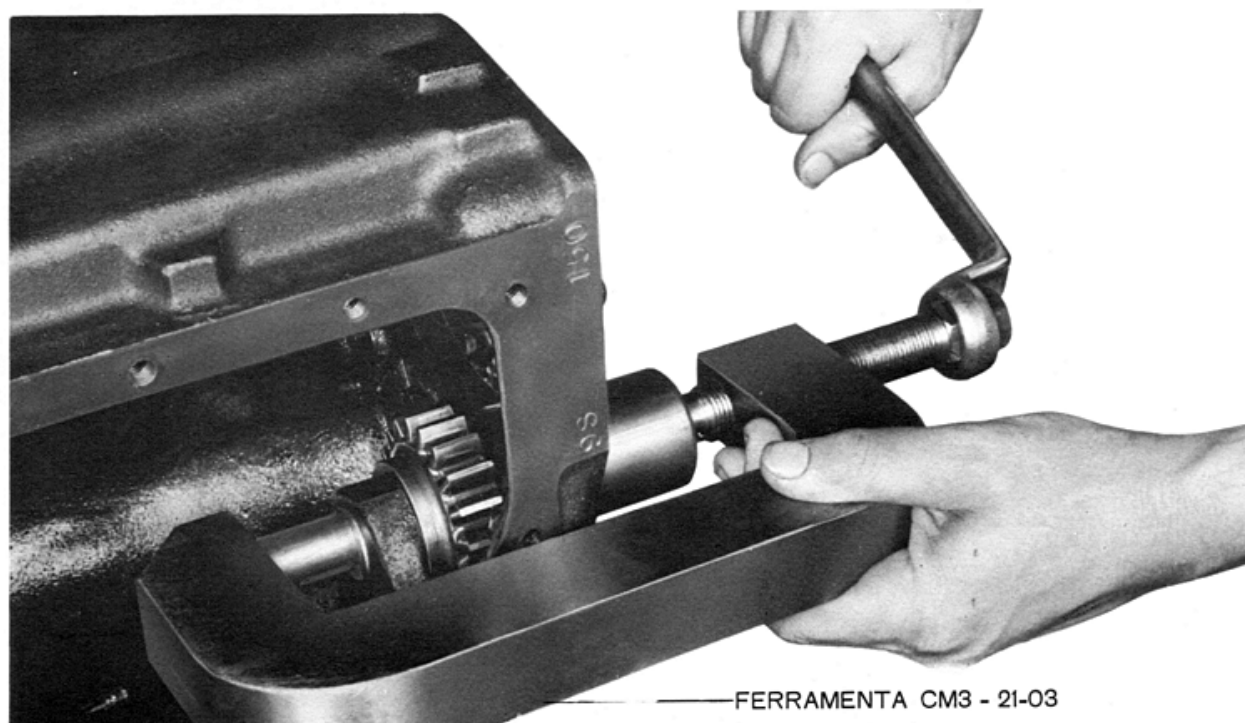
Remoção da engrenagem intermediária de marcha-a-ré
